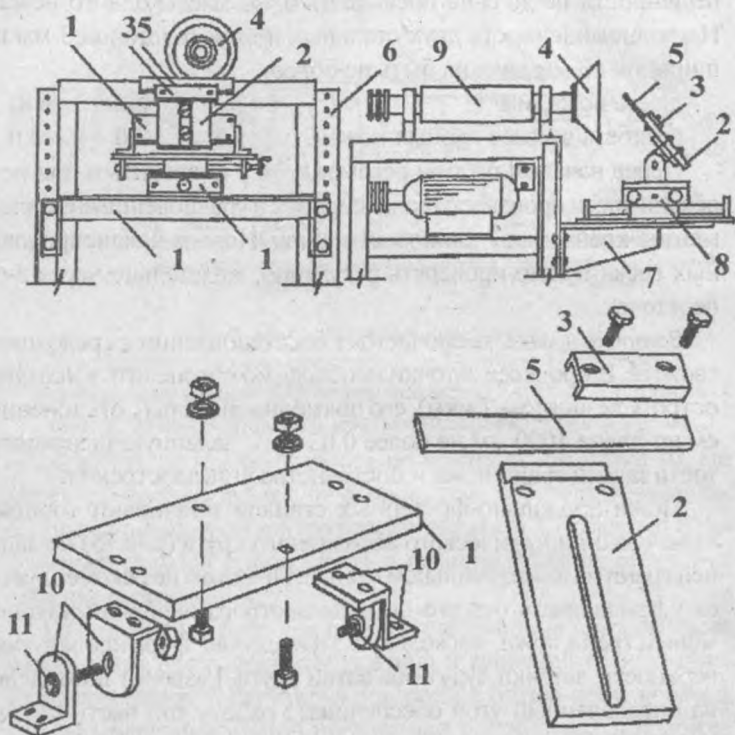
Устройство для заточки строгальных ножей: а-наклонно-поворотная платформа; б-держатель ножа; 1-платформа; 2-держатель ножа; 3-прижимная скоба; 4-чашечный абразивный круг; 5-строгальный нож; 6-технологический уголок; 7-малый пильный стол; 8-двухкоординатный стол; 9-рабочий вал; 10-уголки поворотной платформы; 11-болт
